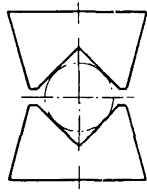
Рекомендуемый профиль контакта нагревательной установки для радиального зажима заготовки
